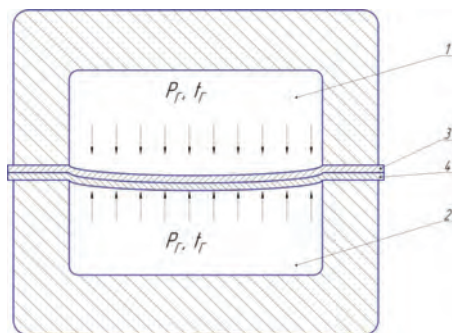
Схема нагружения обрабатываемых заготовок:
